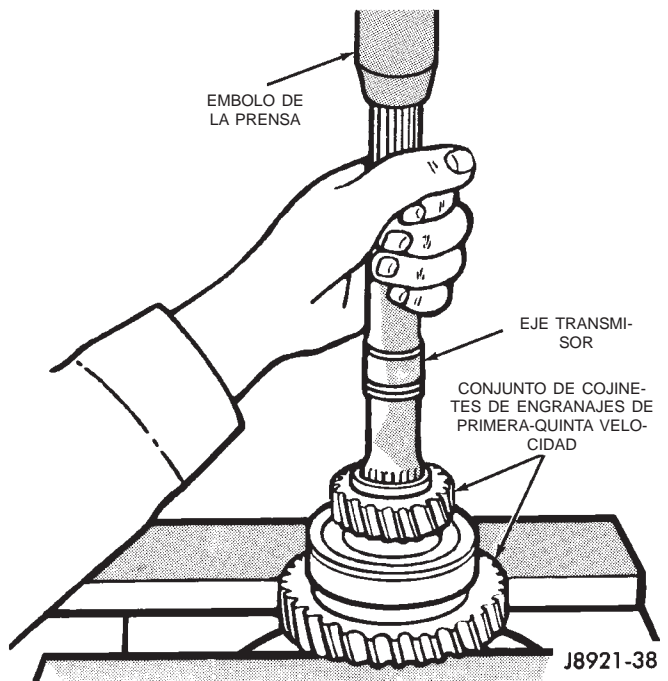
Desmontaje de engranaje de quinta velocidad, cojinete de engranaje de primera velocidad y arandela de empuje
